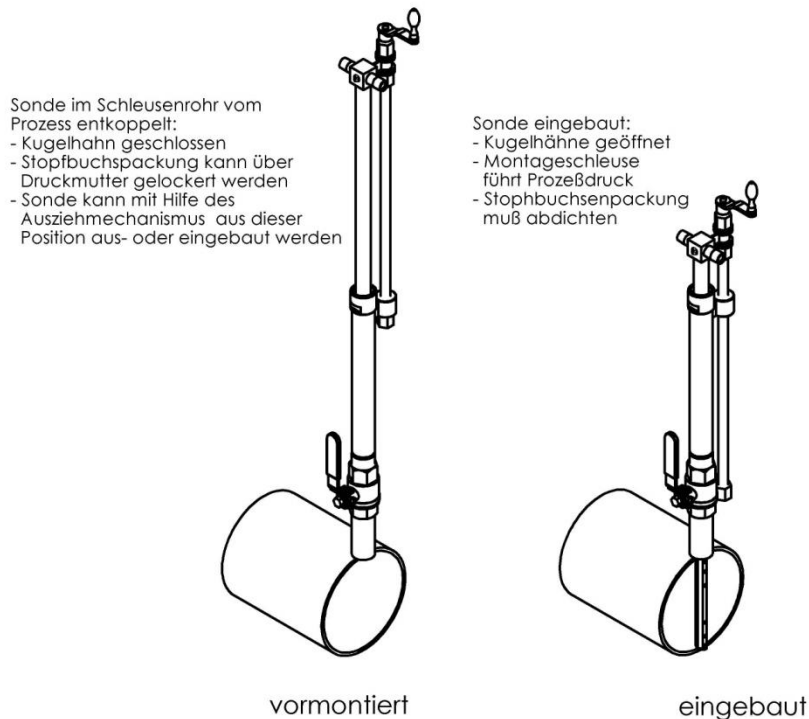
Aufbau einer FASTLOK-N-Sonde
